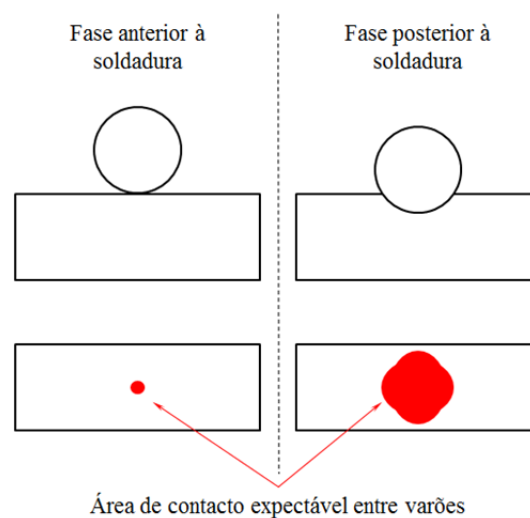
Área de contacto expectável entre varões em diferentes fases da soldadura
